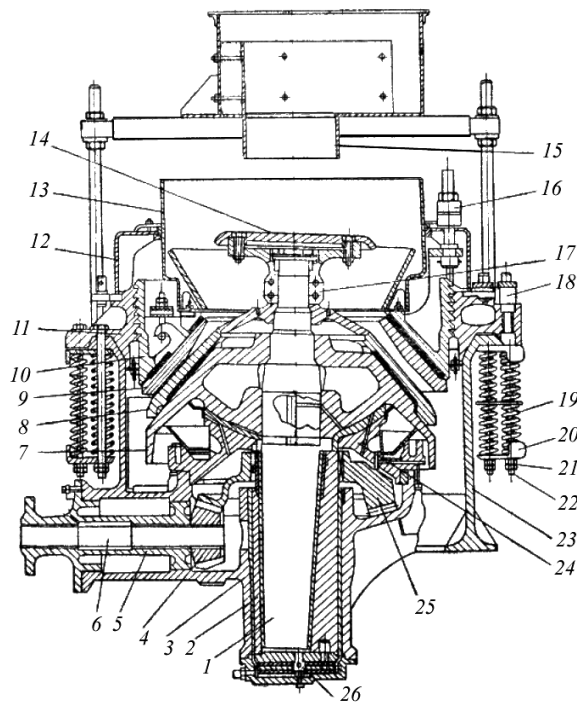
Конусна дробарка для дрібного дроблення:
